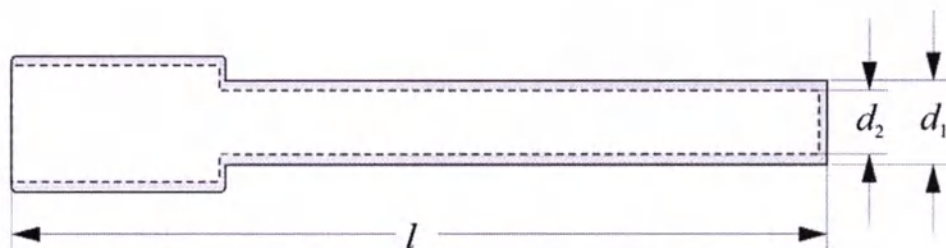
Схема общего вида защитного колпачка для иглы
